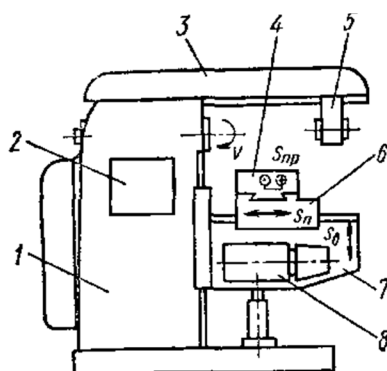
Общий вид горизонтально-фрезерного станка
